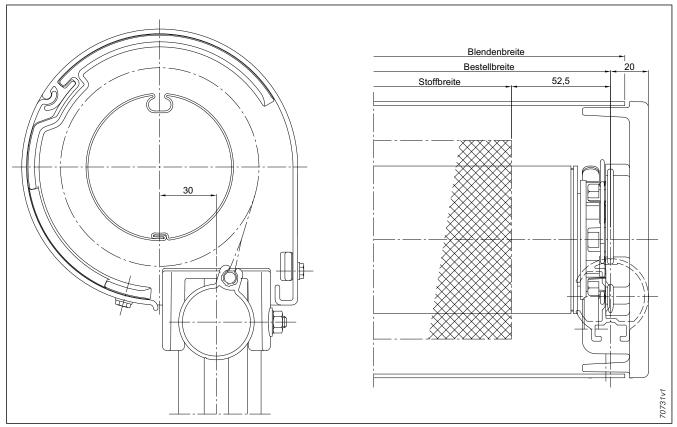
Fassaden-Markise 201 mit Blende Typ 8.3
